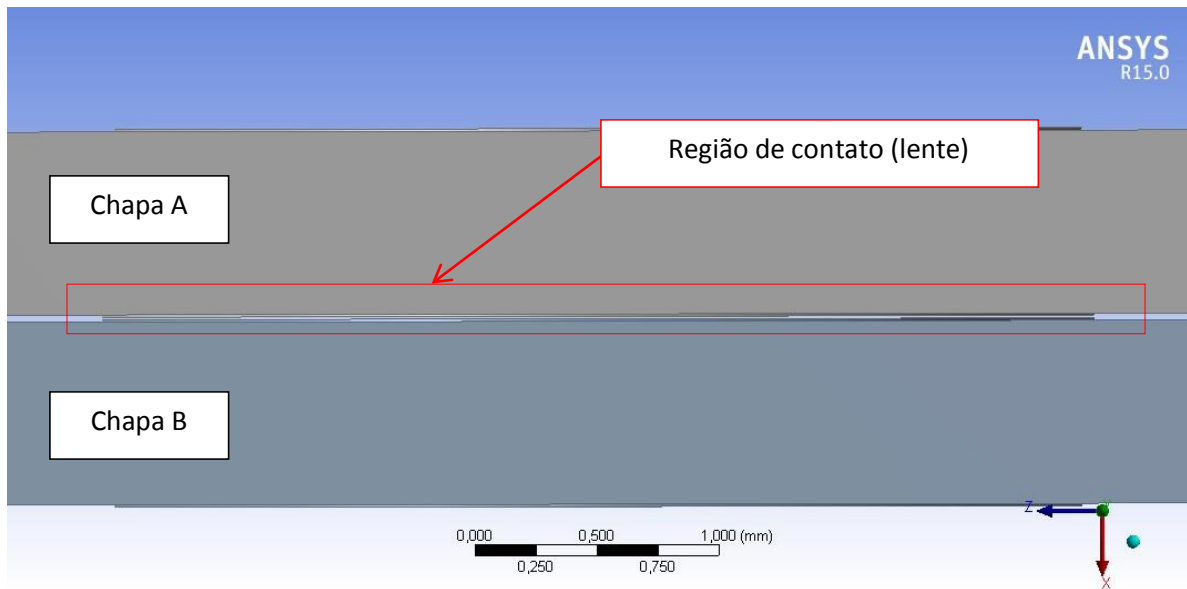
Vista lateral da chapa com espessura das chapas e posição de sobreposição (dimensões em mm).
